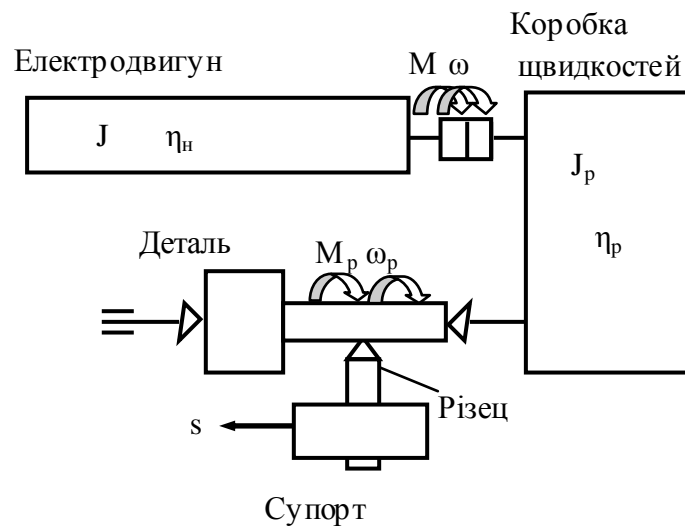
Спрощена кінематична схема приводу головного руху токарного верстата
